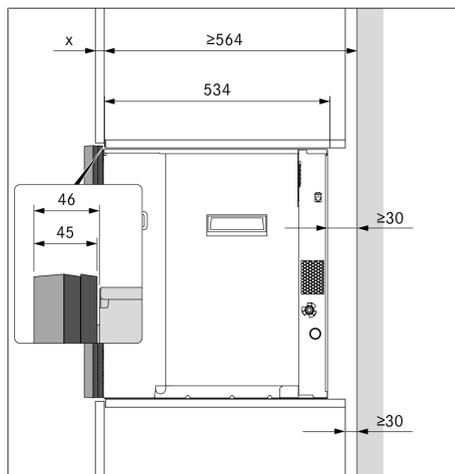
Einbaumaße 2 Rahmen Spacer
